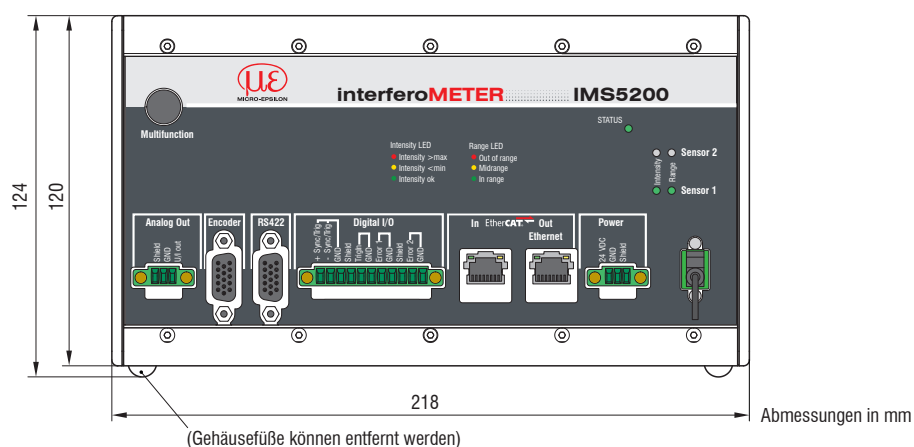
Maßzeichnung Frontansicht des IMC5200 Controllers
